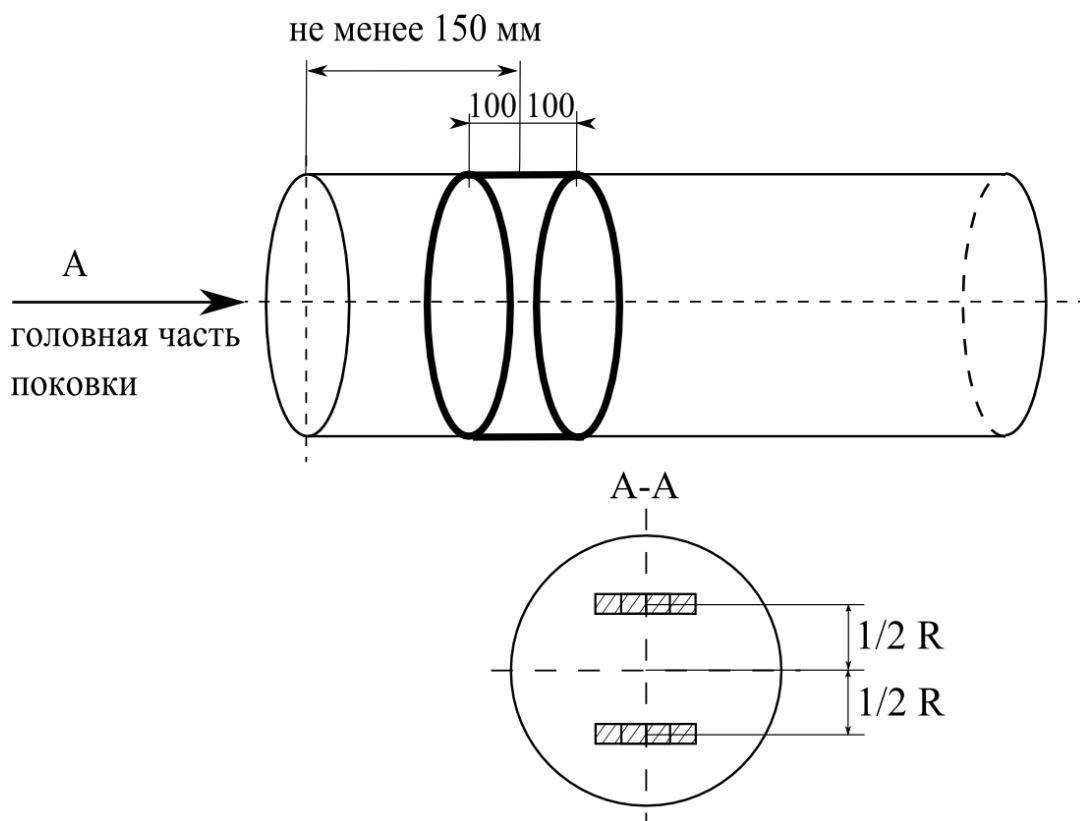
Схема вырезки заготовок для образцов из поковки
